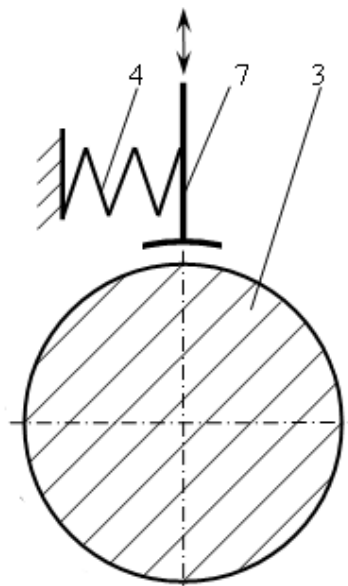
Схема отключения промежуточного вала от корпуса
